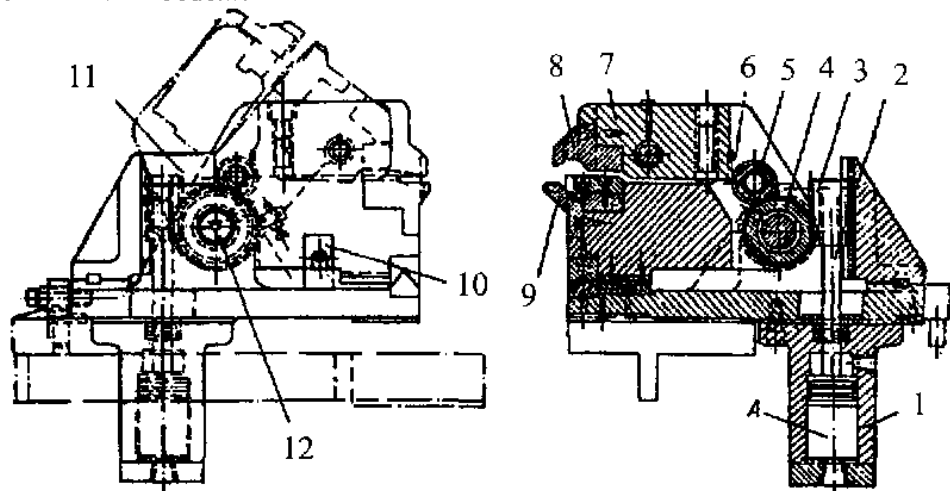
Пристрій для закріплення заготовок при зовнішньому протягуванні
